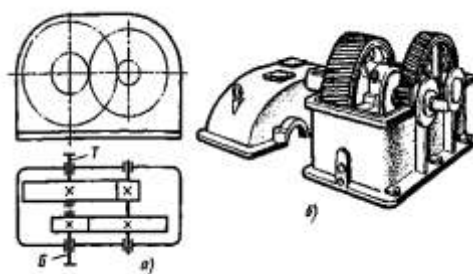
Двухступенчатый горизонтальный соосный редуктор:
